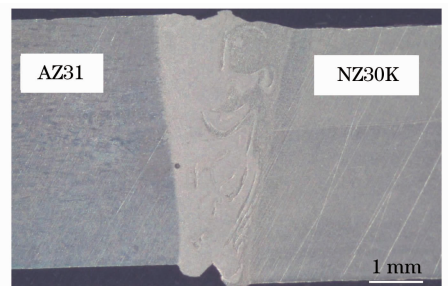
异种镁合金焊接接头横截面宏观形貌
